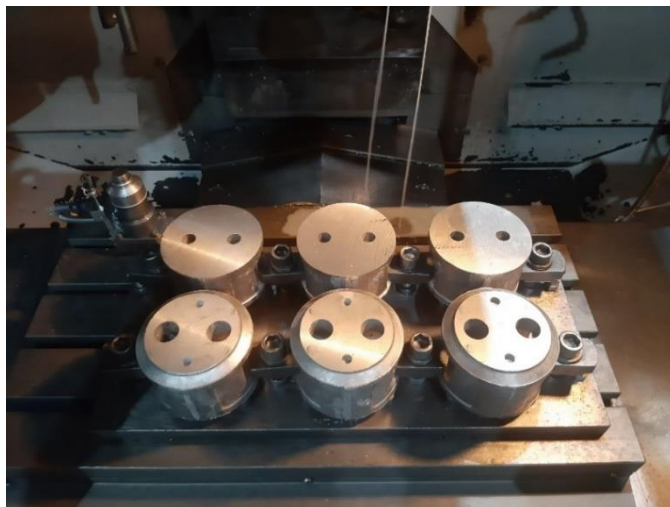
Базування та закріплення заготовок для фрезерної обробки
